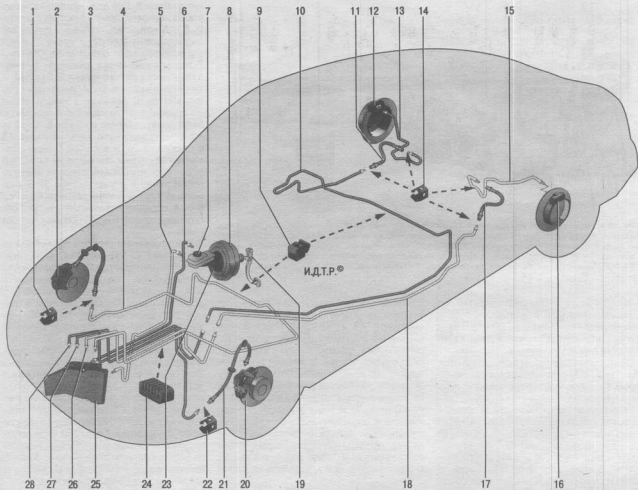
Схема гидропривода тормозов (с антиблокировочной системой): 1, 14, 22 – скобы крепления гибких шлангов; 2 – тормозной механизм правого переднего колеса; 3 – гибкий шланг тормозного механизма правого переднего колеса; 4, 5, 15, 18, 26 – трубопроводы контура правый передний – левый задний тормоза; 6, 10, 13, 27, 28 – трубопроводы контура левый передний – правый задний тормоза; 7 – бачок главного цилиндра гидропривода тормозов; 8 – вакуумный усилитель; 9, 24 – держатели трубопроводов; 11 – гибкий шланг тормозного механизма правого заднего колеса; 12 – тормозной механизм правого заднего колеса; 16 – тормозной механизм заднего левого колеса; 17 – гибкий шланг тормозного механизма левого заднего колеса; 19 – педаль тормоза; 20 – тормозной механизм левого переднего колеса; 21 – гибкий шланг тормозного механизма левого переднего колеса; 23 – главный цилиндр гидропривода тормозов; 25 – гидроэлектронный модуль АБС
